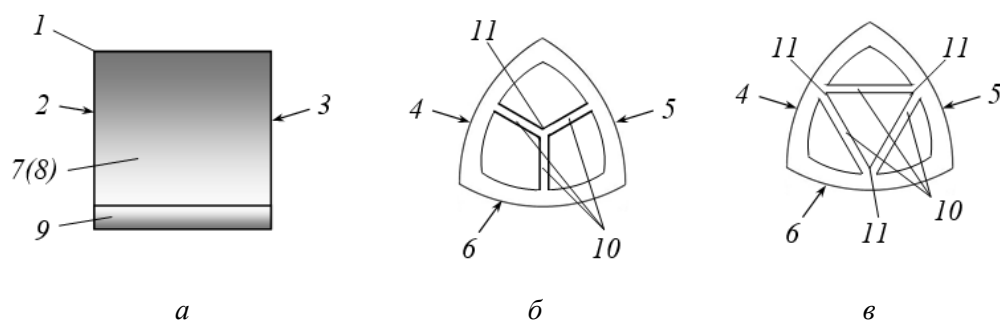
Конструкція елемента насадки (пояснення в тексті): *а* – загальний вигляд елемента насадки, *б* і *в* – вигляд насадки з боку однієї з основ, приклади виконання поздовжніх перегородок
